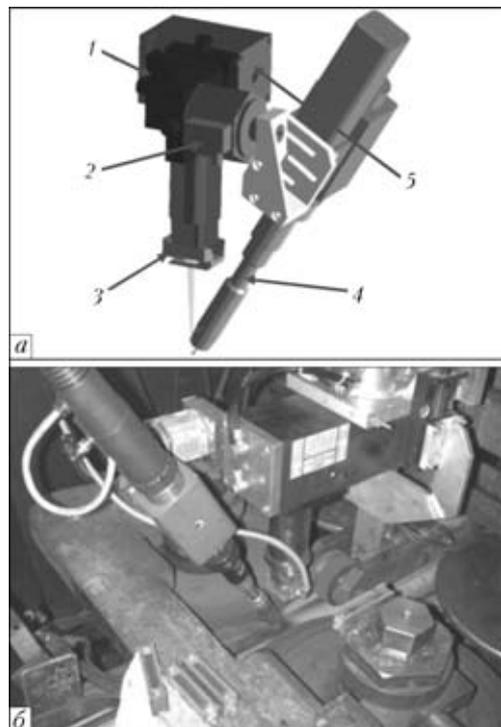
Сварочная головка, используемая при гибридном процессе сварки CO₂-лазером, в проектном (а) и промышленном (б) исполнении: 1 — блок регулировки; 2 — противоударная система; 3 — пересекающая струя; 4 — газовая горелка для дуговой сварки плавящимся электродом в среде защитного газа; 5 — фокусирующее зеркало
